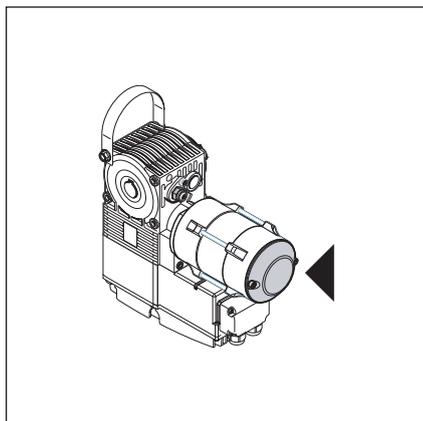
Wellenantrieb mit Abdeckkappe
